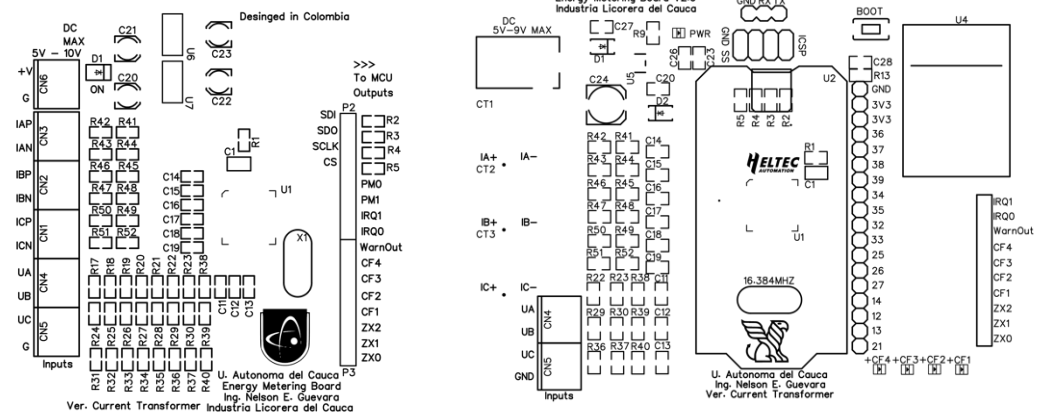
Máscara de componentes PCB V1.0 y V2.0. Fuente propia.
